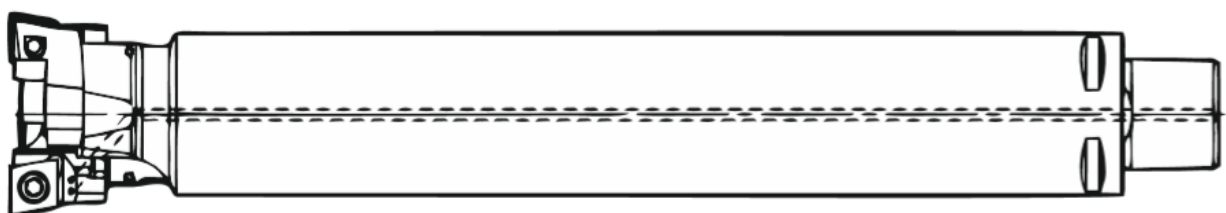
Антивібраційний інструмент “CoroBore BR20” з двома різальними кромками [9, ст.268]
